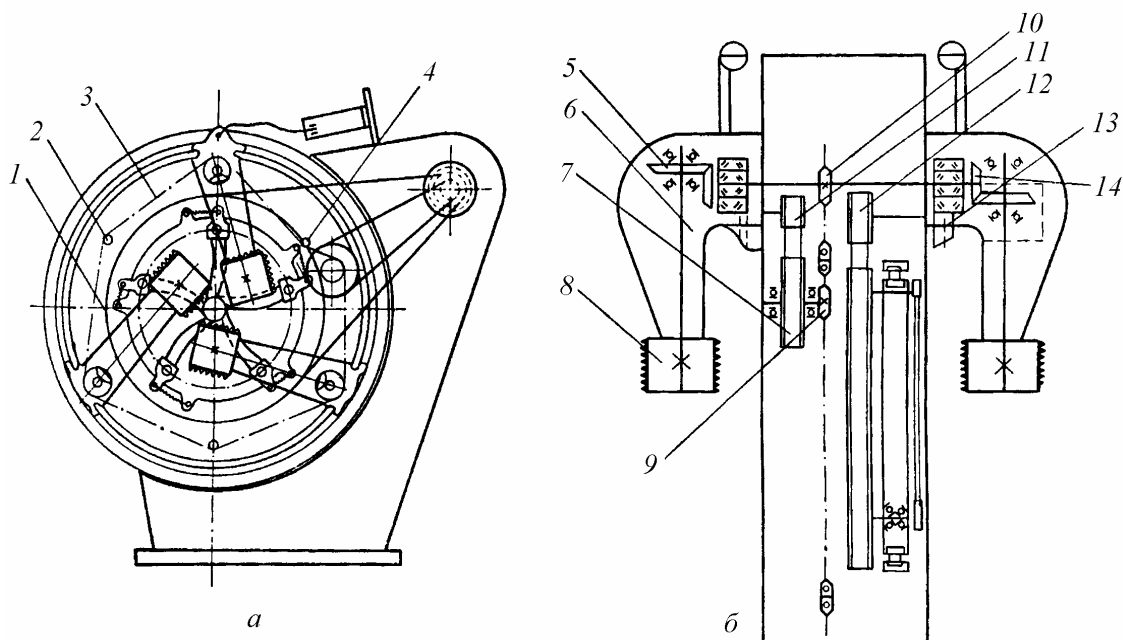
Кинематическая схема окорочного станка ОК-35М: *а* – механизм привода ротора; *б* – механизм подачи
